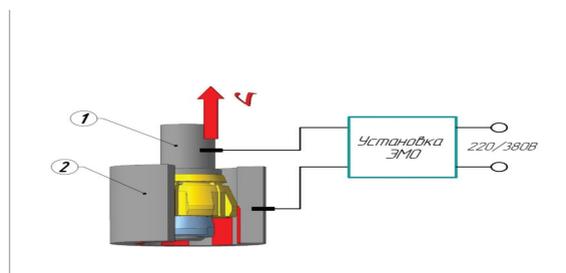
Дорн для выборочной электромеханической закалки внутренних поверхностей деталей
